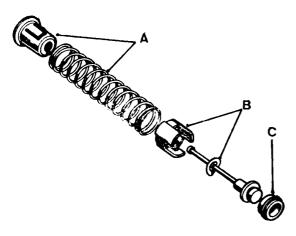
12 - Desmontaje de la válvula del cilindro.
